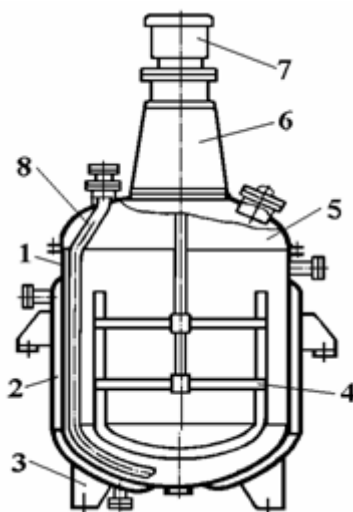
Будова реактора з рамною мішалкою: 1 - корпус; 2 - сорочка; 3 - опора; 4 - мішалка рамна; 5 - кришка знімна; 6 - редуктор; 7 - електродвигун; 8 - труба для передавлювання середовища
